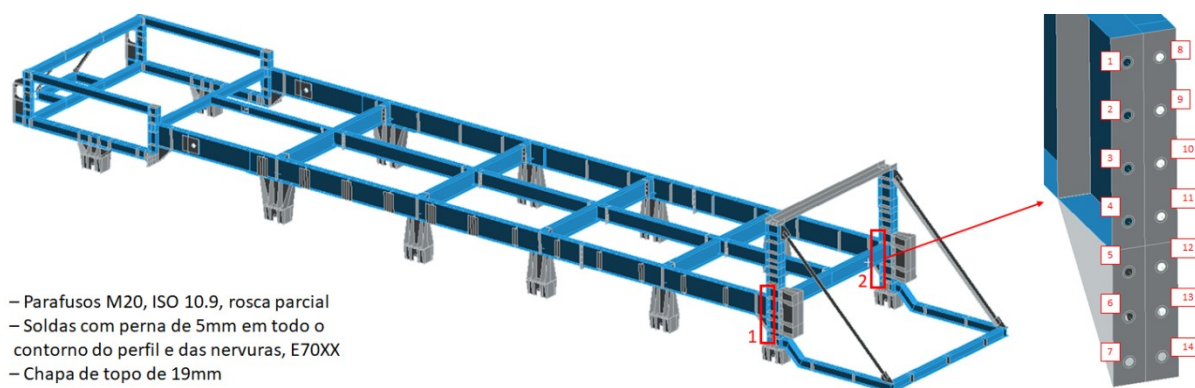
Ligação do chassi I – Ligação entre a viga longitudinal principal e a coluna da descarga.
